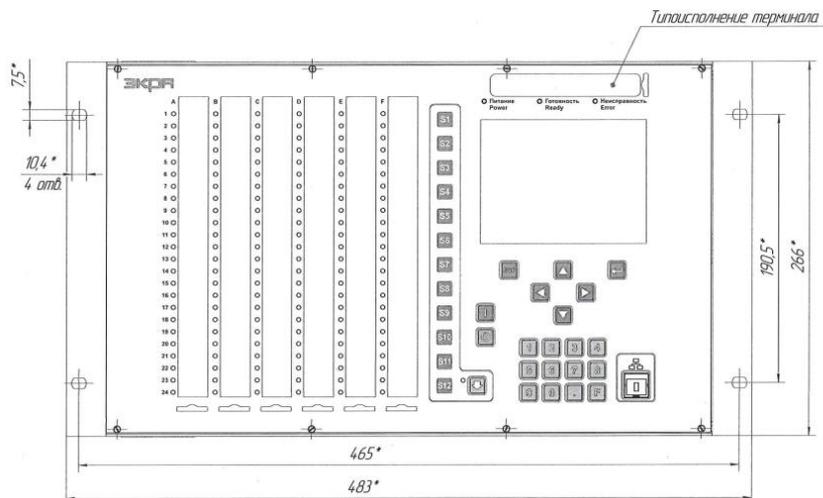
Габаритные и установочные размеры ЭКРА 253 01XX (вид спереди)
